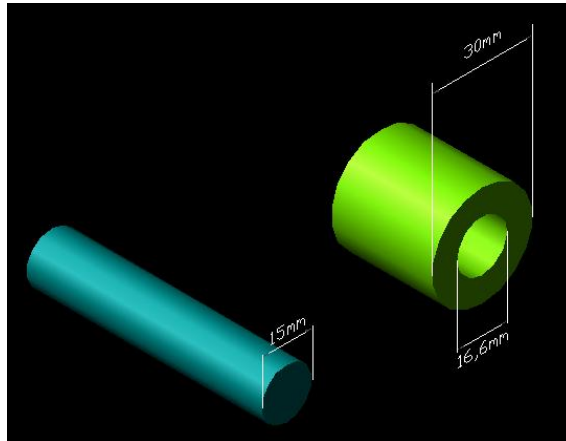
Dimensiones del rodamiento inferior del dispositivo móvil.
